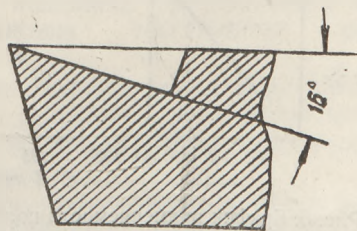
Фрезеровка гнезда под пластинку твердого сплава (угол вреза пластинки  $\gamma_{вр} = 16^\circ$ )
